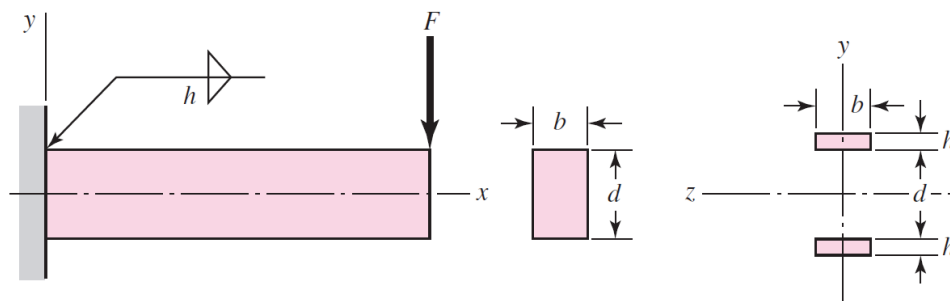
Voladizo de sección transversal rectangular soldado.
